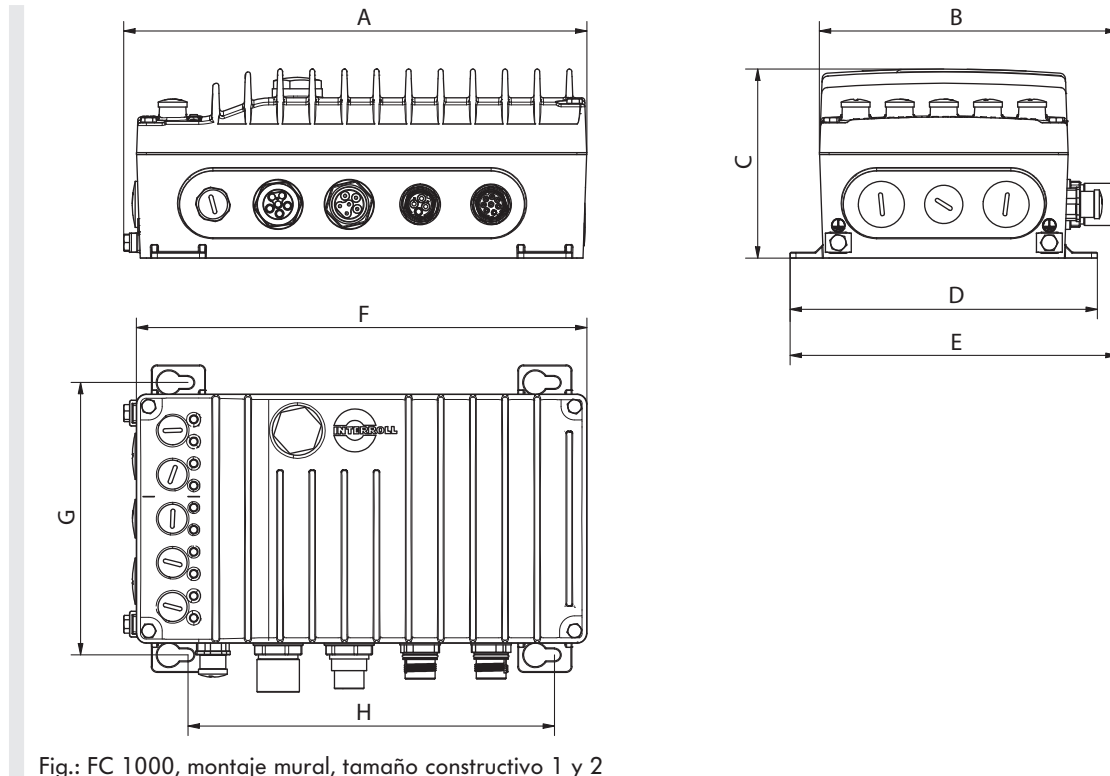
, montaje mural, tamaño constructivo 1 y 2
